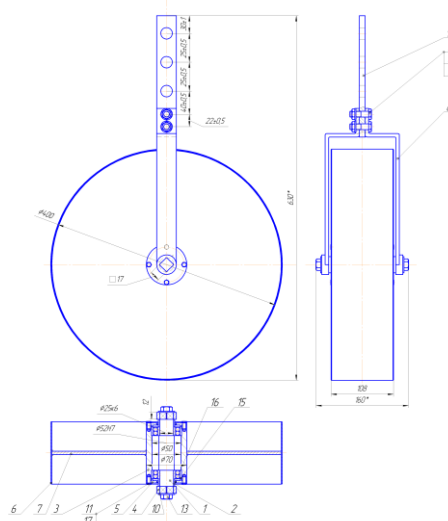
Колесо опорне: 1 – вісь; 2 – втулка; 3 – корпус підшипника; 4 – корпус; 5 – кришка; 6 – обід; 7 – опора; 8 – кронштейн; 9 – стійка; 10 – шайба; 11,12,13 – болти; 14 – гайка; 15 – підшипник; 16 – манжета; 17,18 – шайби
